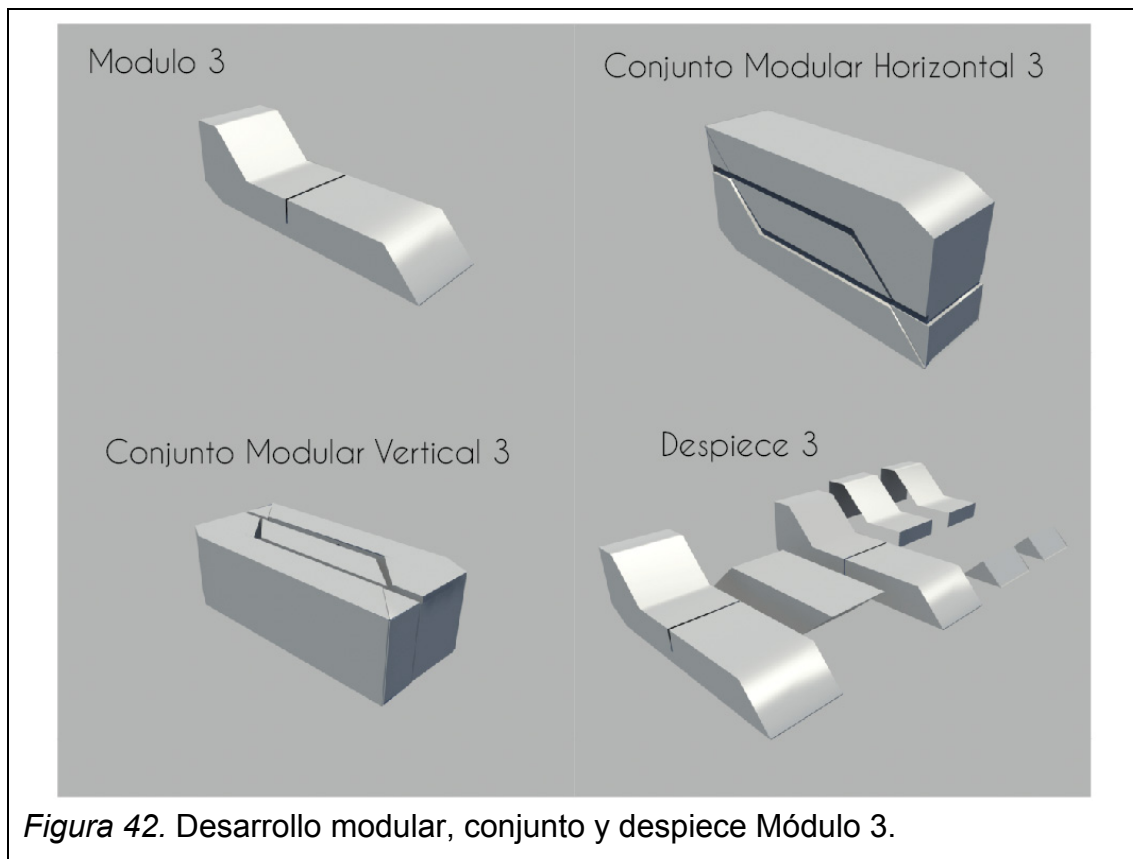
Desarrollo modular, conjunto y despiece Módulo 3.
